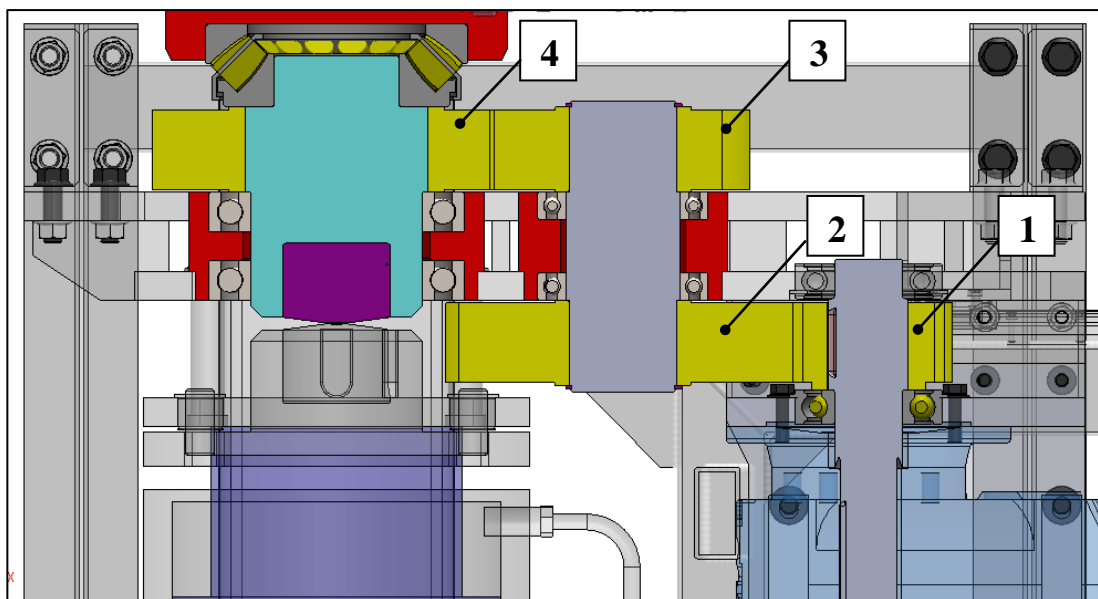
Vista esquemática em corte de seção transversal do conjunto de transmissão por engrenagens
